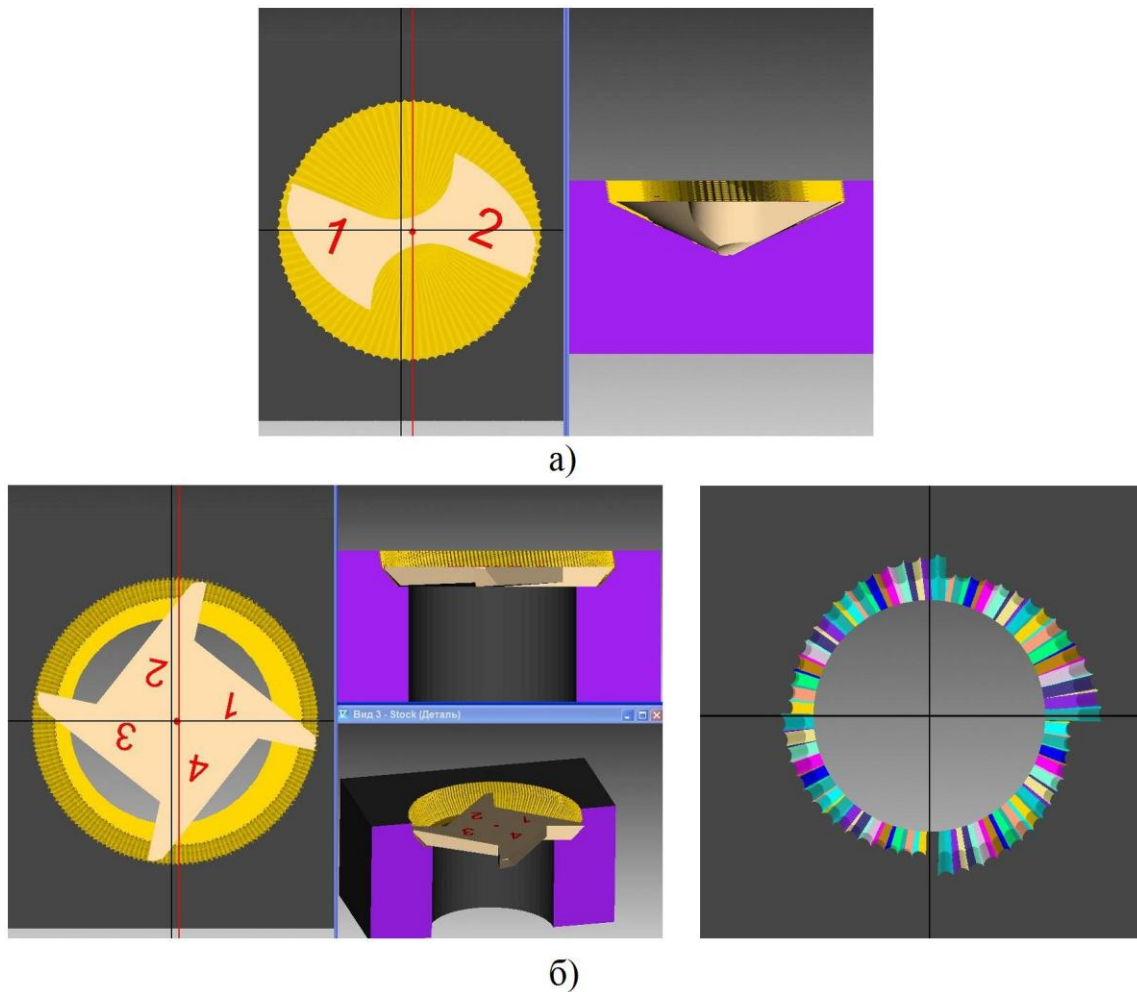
Реальная форма и шероховатость отверстий, полученная по заданным режимам резания: а – сверлом, б – разверткой
